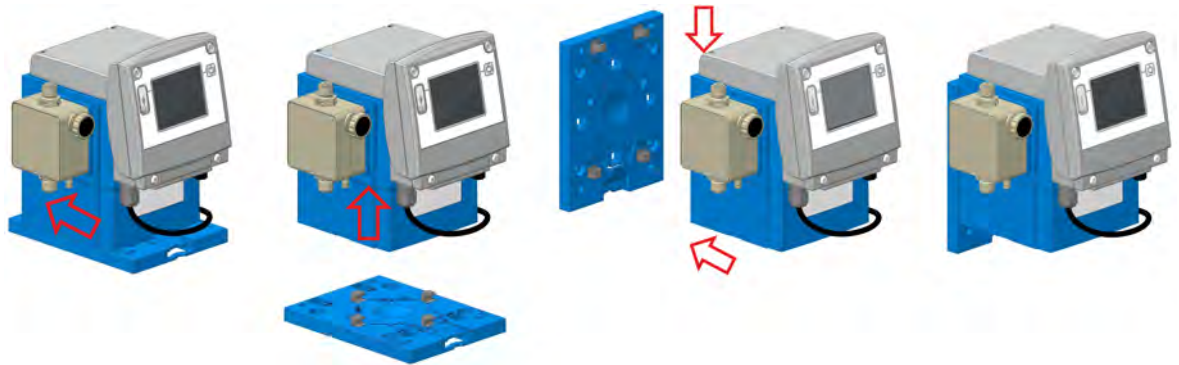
Passaggio da montaggio su tavolo (in verticale, ad esempio su pavimento, console o tanica) per il montaggio a parete (appesa)
